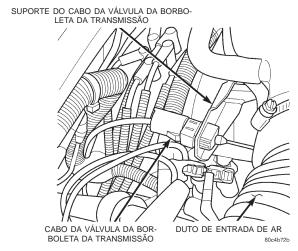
A Remoção/Instalação do Cabo da Válvula da Borboleta
